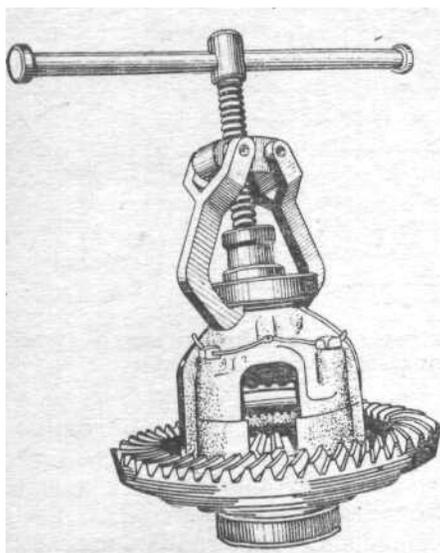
Съемник внутреннего кольца подшипника коробки дифференциала
